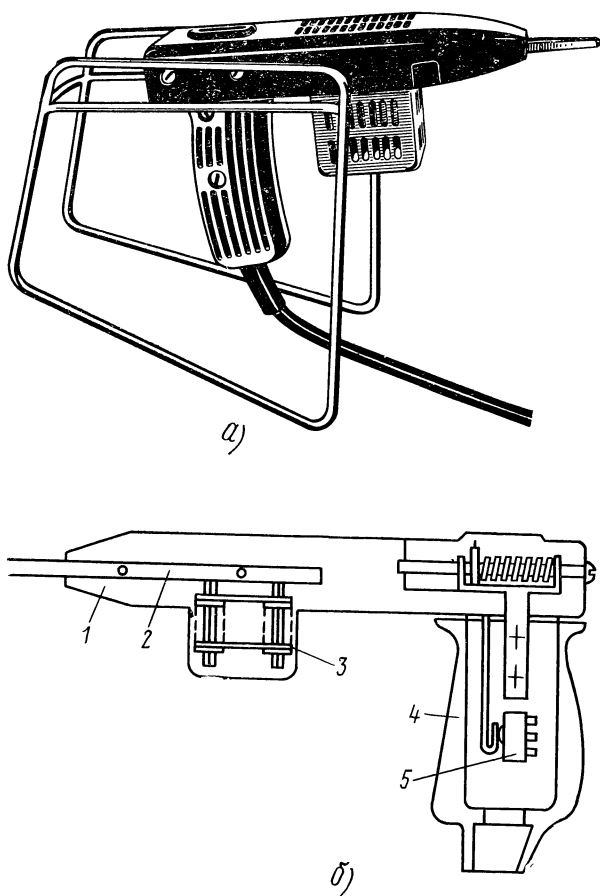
Ультразвуковой сварочный пистолет:
